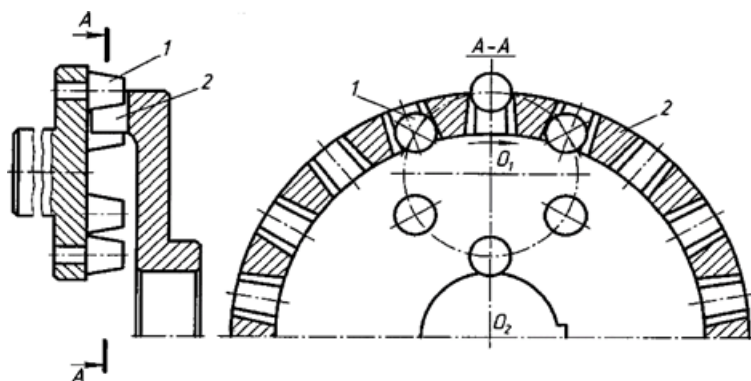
Торцевая передача Нечаева: 1 - шестерня, 2 зубчатое колесо
